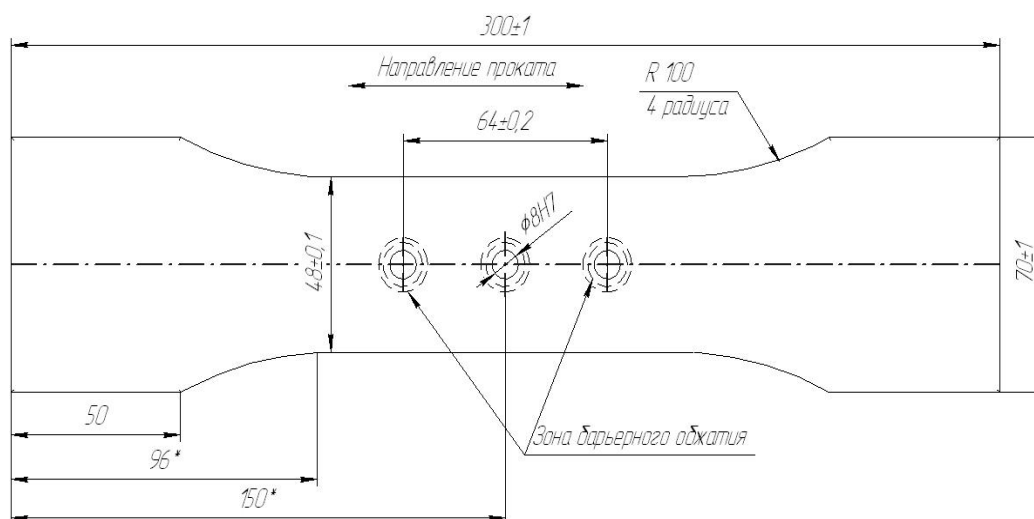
Геометрические размеры заготовки для изготовления образцов
